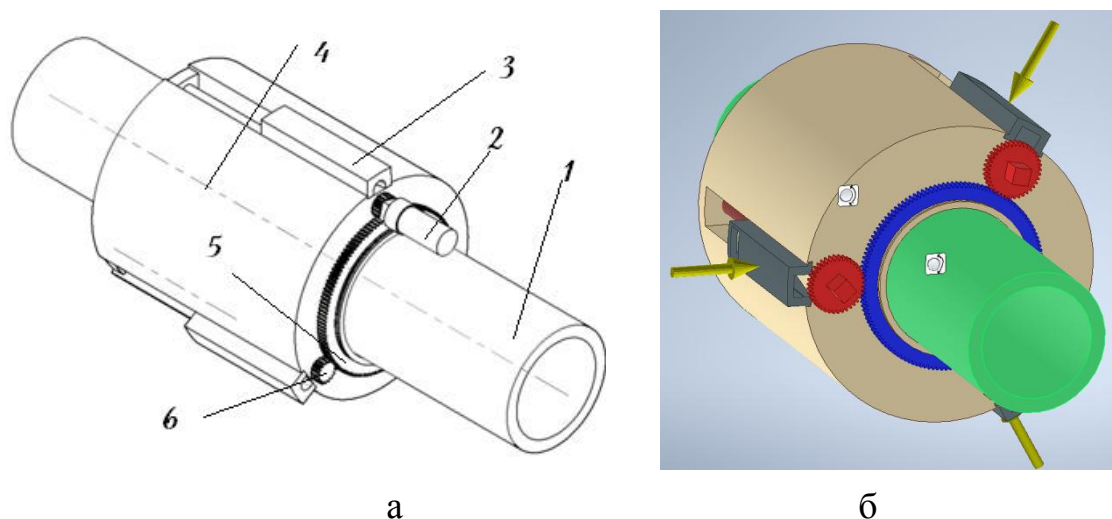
Клиновий пристрій підтримки борштанги; а – конструктивна схема; б – 3D-модель, побудована засобами Autodesk Inventor.
